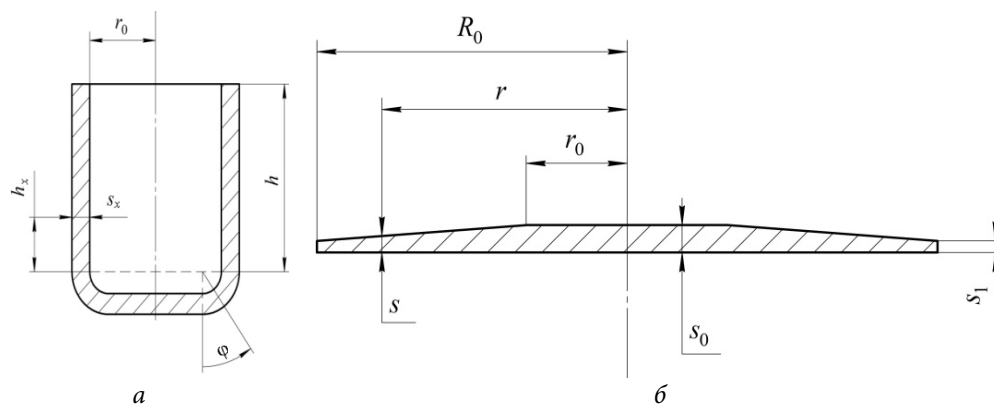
Схемы вытягиваемой детали (а) и применяемой дисковой заготовки (б)
